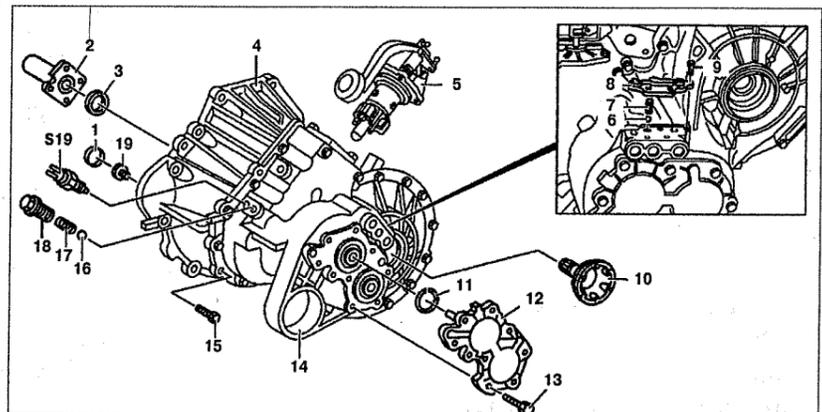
Разборка и сборка коробки передач (автомобили с двигателями 111.948 и 601.970): 1. Задняя крышка вала заднего хода, 2. Направляющая труба, 3. Фиксатор, 4. Корпус сцепления, 5. Узел переключения передач, 6, 16. Шарик, 7, 17. Пружина, 8. Крышка замка блокировки переключения передач, 9, 13, 15, 19. Болт, 10. Выходной фланец, 11. Стопорное кольцо, 12. Крышка подшипников, 14. Корпус коробки передач, 18. Блокировочный болт замка блокировки переключения передач, S19. Выключатель фонарей заднего хода.
